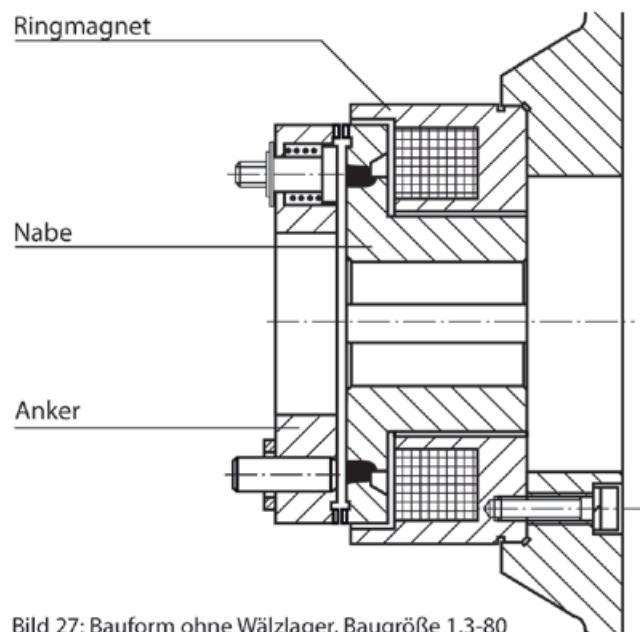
Bauform ohne Wälzlager, Baugröße 1,3-80
